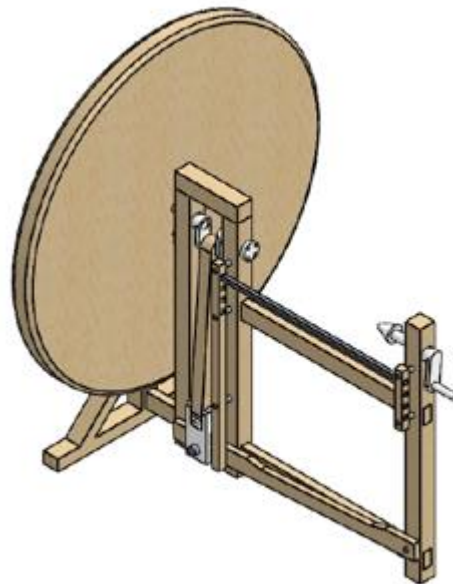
Ensamblaje del Torno sin pieza a tornear. Fuente: Elaboración propia
